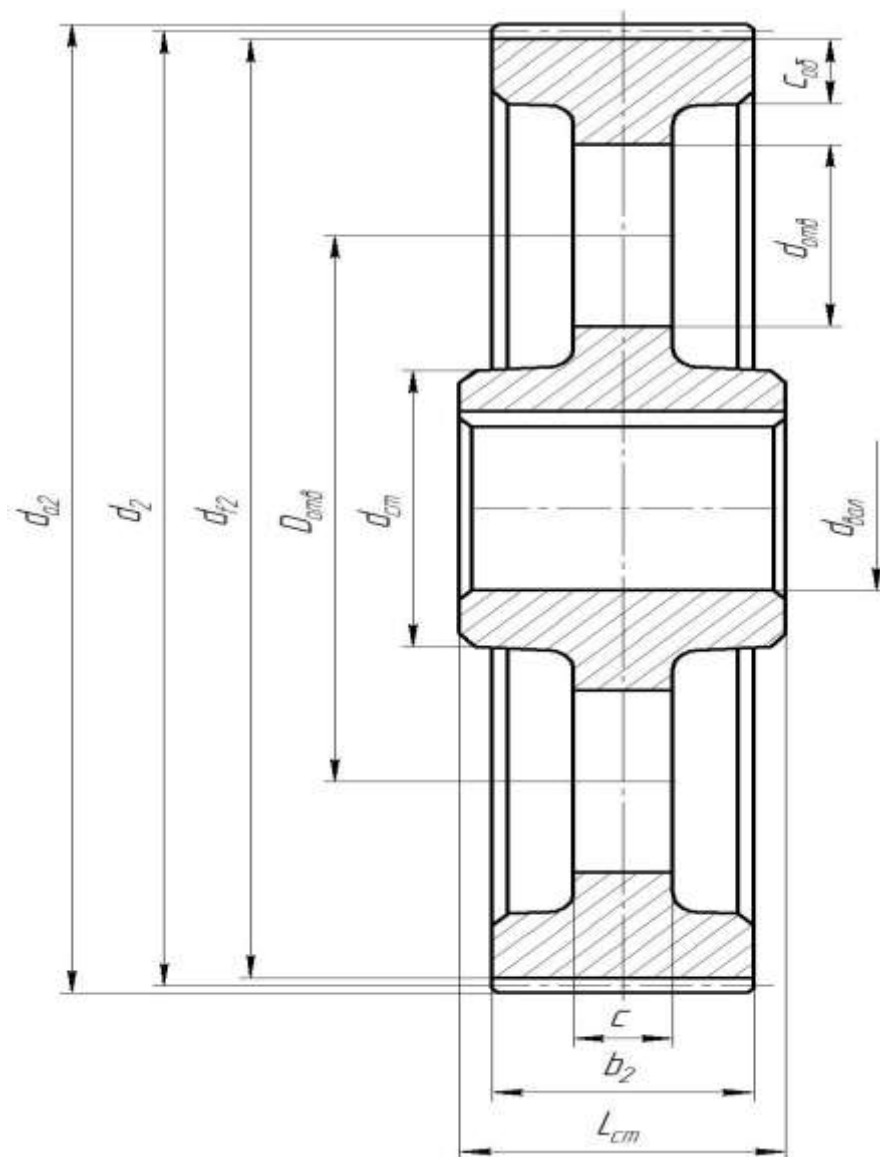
Конструкция зубчатого колеса (чертеж)
